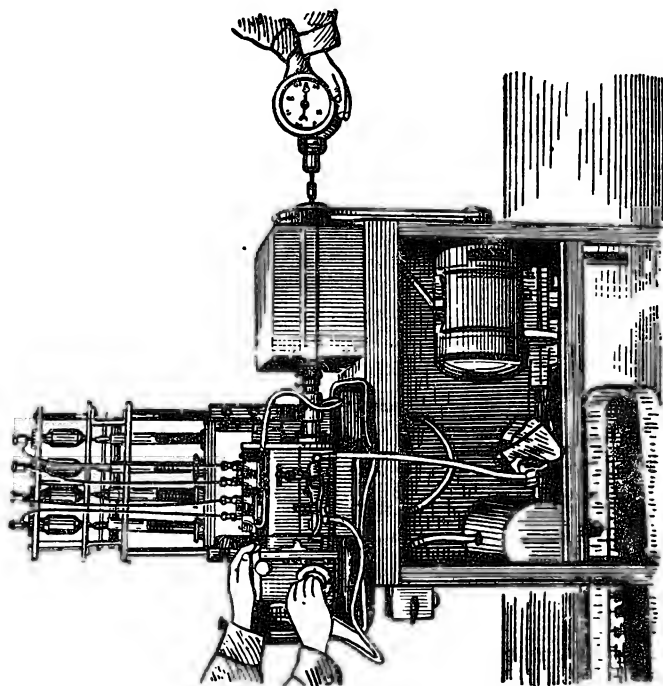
Проверка равномерности подачи топлива отдельными плунжерными парами
